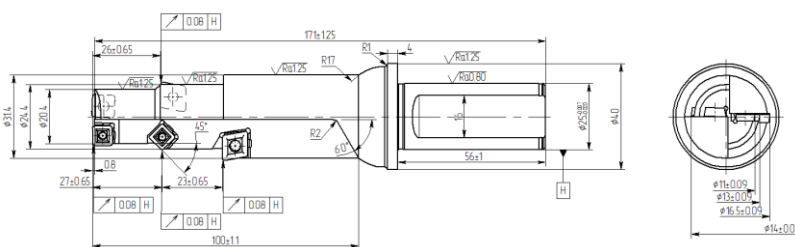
Чертеж сборного четырёхступенчатого сверла
